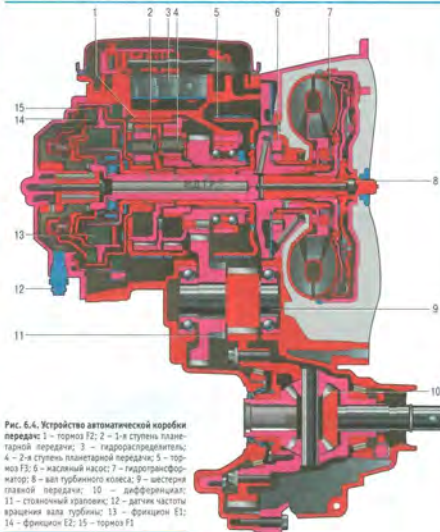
Устройство автоматической коробки передач: 1 – тормоз F2; 2 – 1-я ступень планетарной передачи; 3 – гидрораспределитель; 4 – 2-я ступень планетарной передачи; 5 – тормоз F3; 6 – масляный насос; 7 – гидротрансформатор; 8 – вал турбинного колеса; 9 – шестерня главной передачи; 10 – дифференциал; 11 – стояночный храповик; 12 – датчик частоты вращения вала турбины; 13 – фиксатор E1; 14 – фиксатор E2; 15 – тормоз F1
